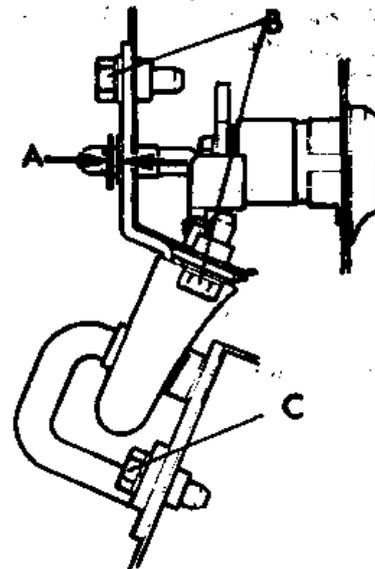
Болты крепления замка багажника (В), зазор для пружинного клипса (А) и болты крепления фиксатора (С) (Разд. 16 и 17)
